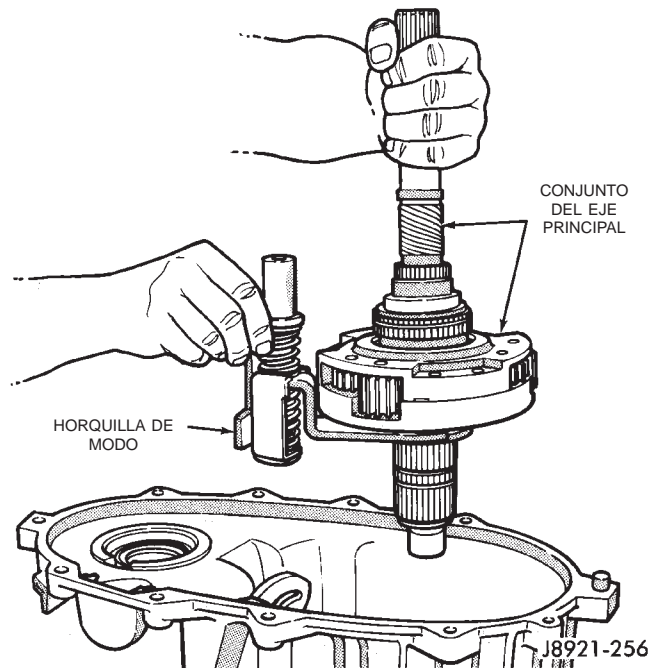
Instalación de eje principal y horquilla de modo ensamblados
